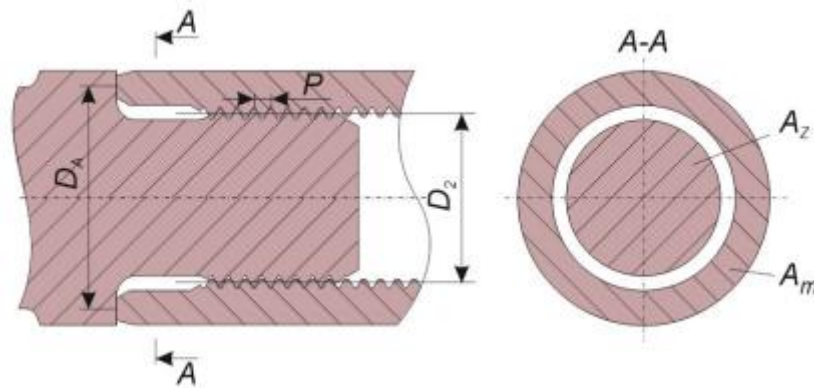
Розрахункова схема різьби насосної штанги
